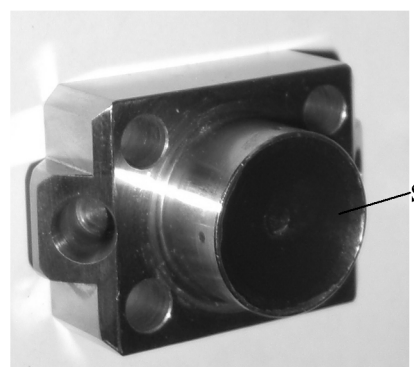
Вставка із сформованою сферичною поверхнею
